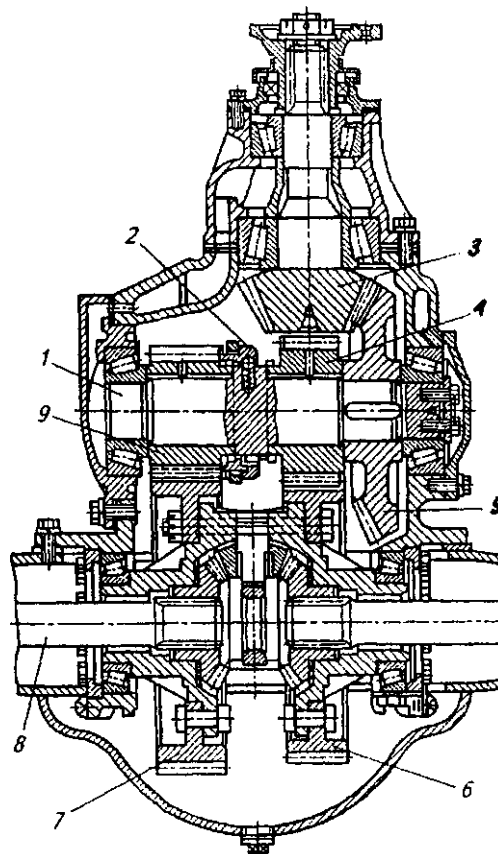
Двухскоростная главная передача: 1 — промежуточный вал; 2 — зубчатая муфта переключения; 3 — ведущая коническая шестерня; 4, 6, 7, 9 — цилиндрические шестерни; 5 — ведомая коническая шестерня; 8 — полуось
